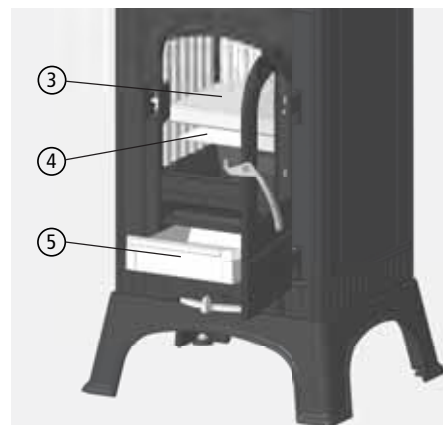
Insérer la pierre de fond, la tôle de fond et le cendrier
